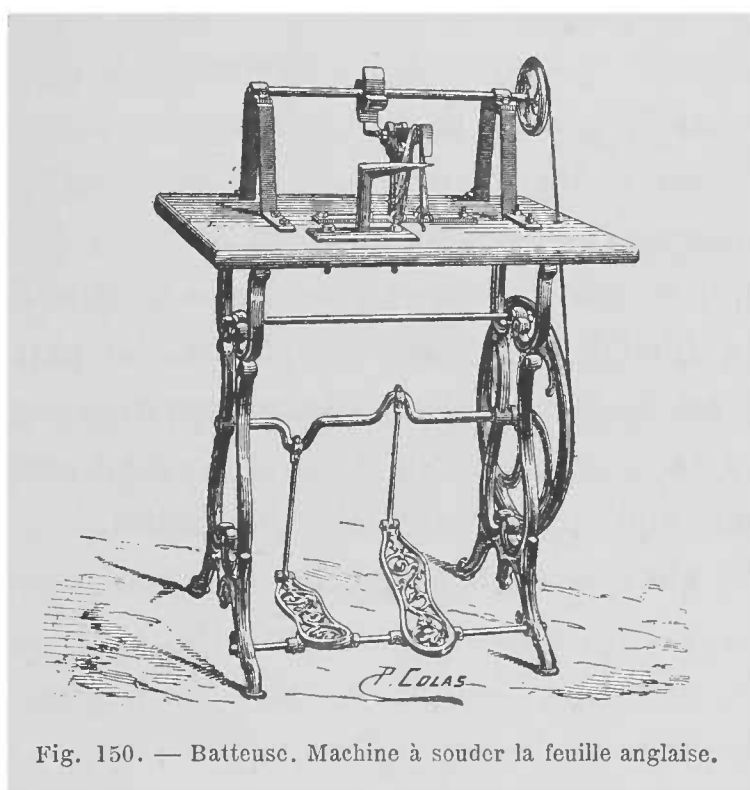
Batteuse. Machine à souder la feuille anglaise.
